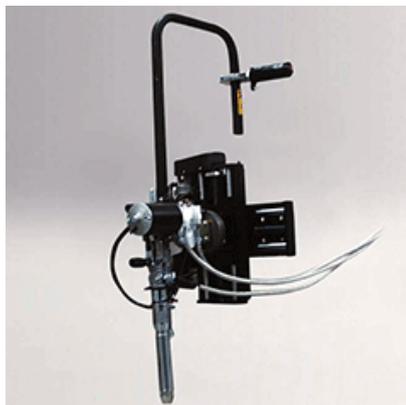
Автомат для дуговой сварки A2 S GMAW MiniMaster
